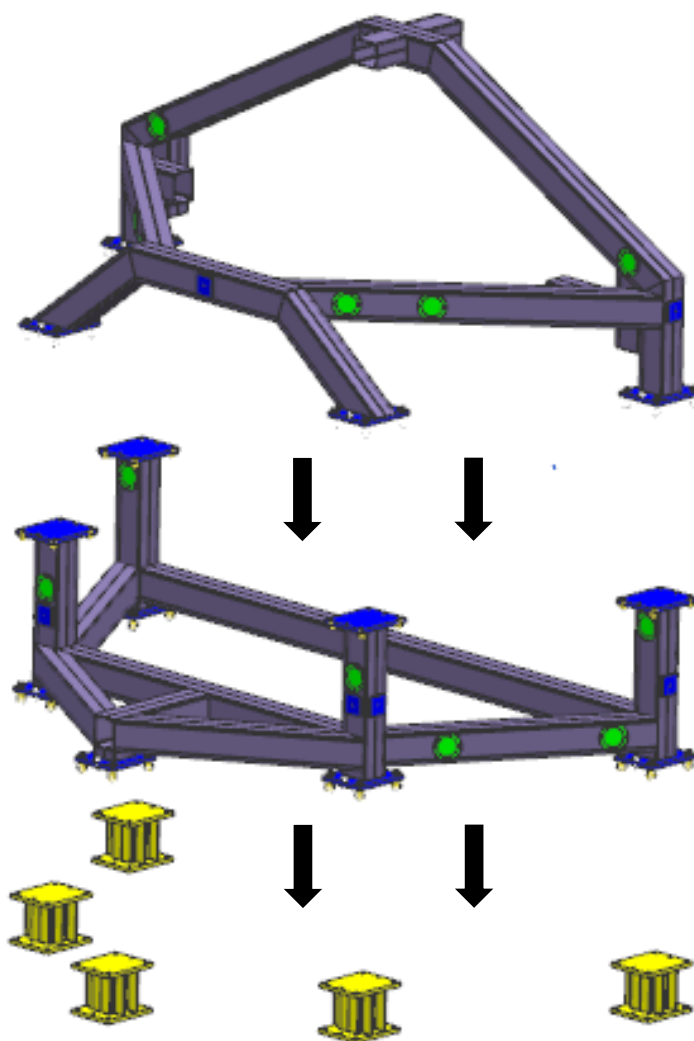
Монтаж каркаса сборочного приспособления.
